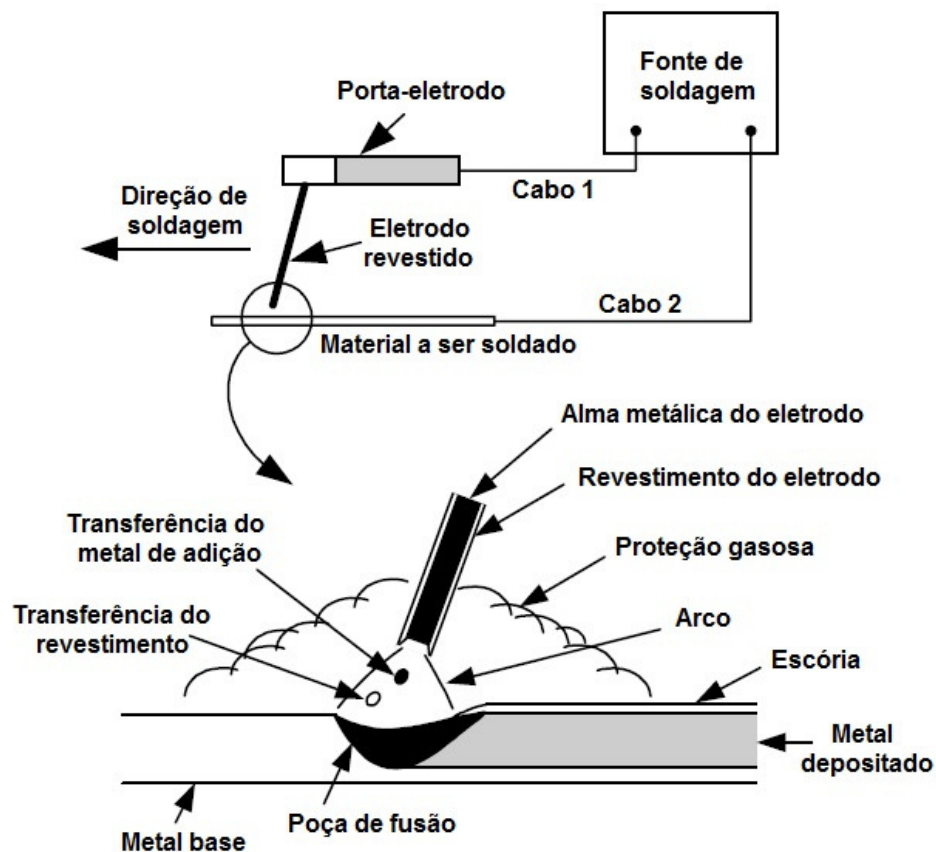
Desenho esquemático do processo de soldagem por eletrodo revestido.
